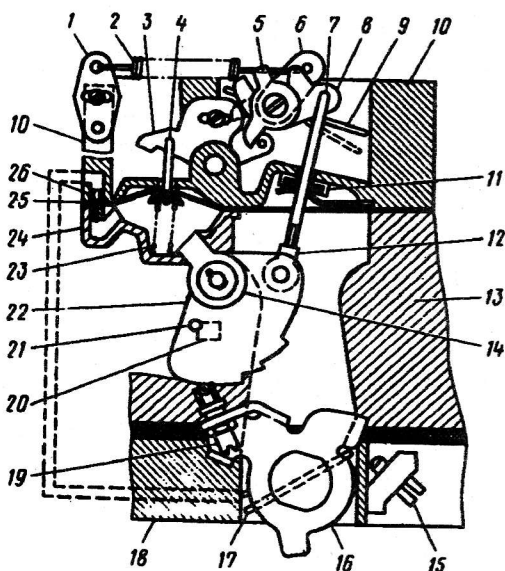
Схема полуавтоматического устройства пуска и прогрева:
